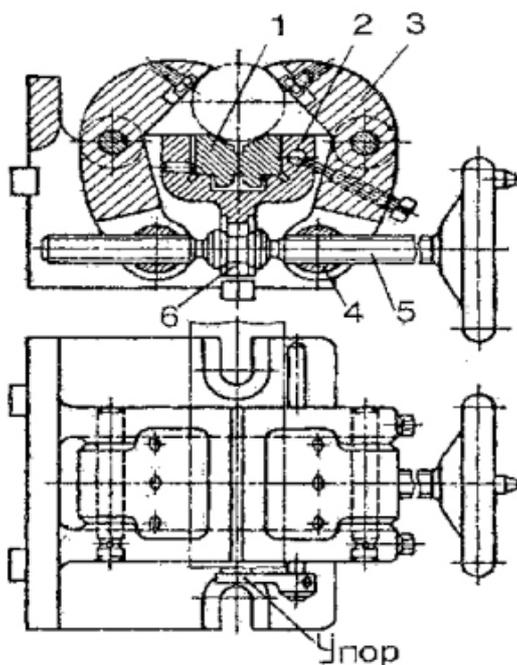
Конструкция самоцентрирующих тисков: 1 – сменная призма; 2 – корпус; 3 – рычаги; 4 – плавающие гайки; 5 – винт; 6 – подшипник.
